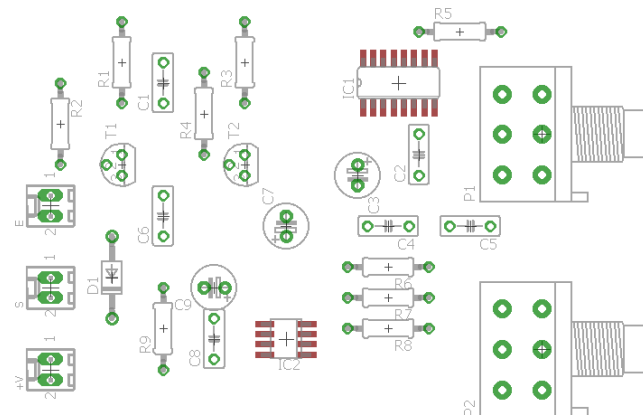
Posicionamento dos componentes para a placa PCB (*Layout*)
